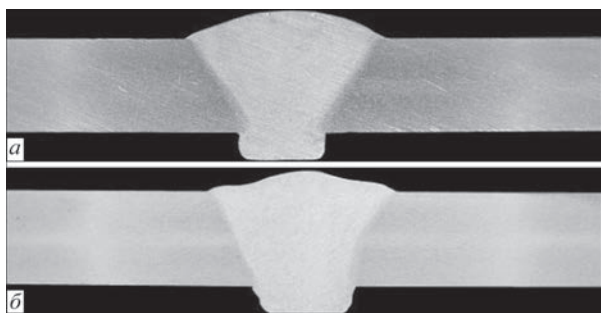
Поперечные шлифы сварных соединений алюминиевого сплава 5083 толщиной 8 мм, полученные сваркой плавящимся электродом (а) на скорости 5 мм/с и гибридной плазменно-дуговой сваркой (б) плавящимся электродом
